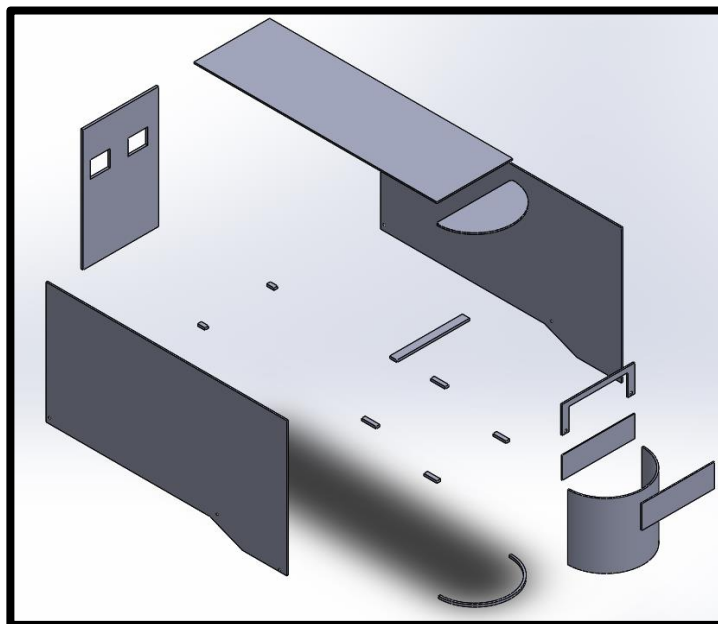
Vista explosionada de las partes de la carcasa. Fuente: Propia.
